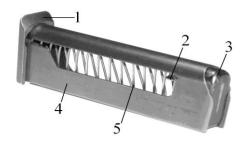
Магазин: 1 – крышка; 2 – зуб подавателя; 3 – подаватель; 4 – корпус; 5 – пружина
